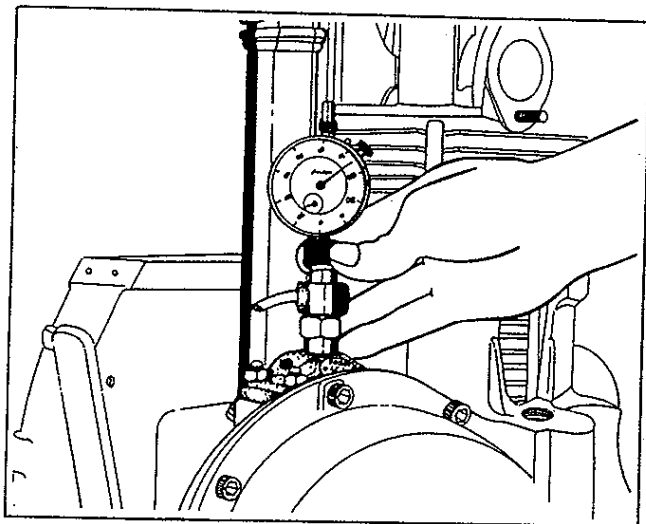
Instalação do dispositivo p/regulagem do ponto de injeção
